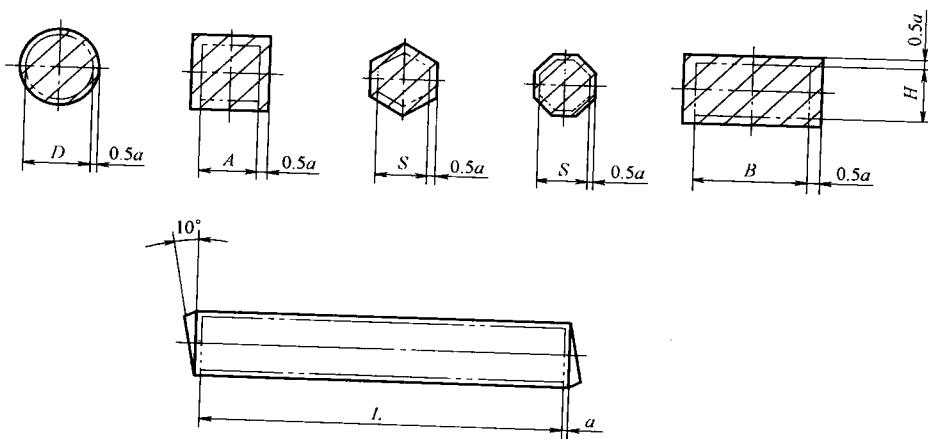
光轴类自由锻件的机械加工余量与公差图例
